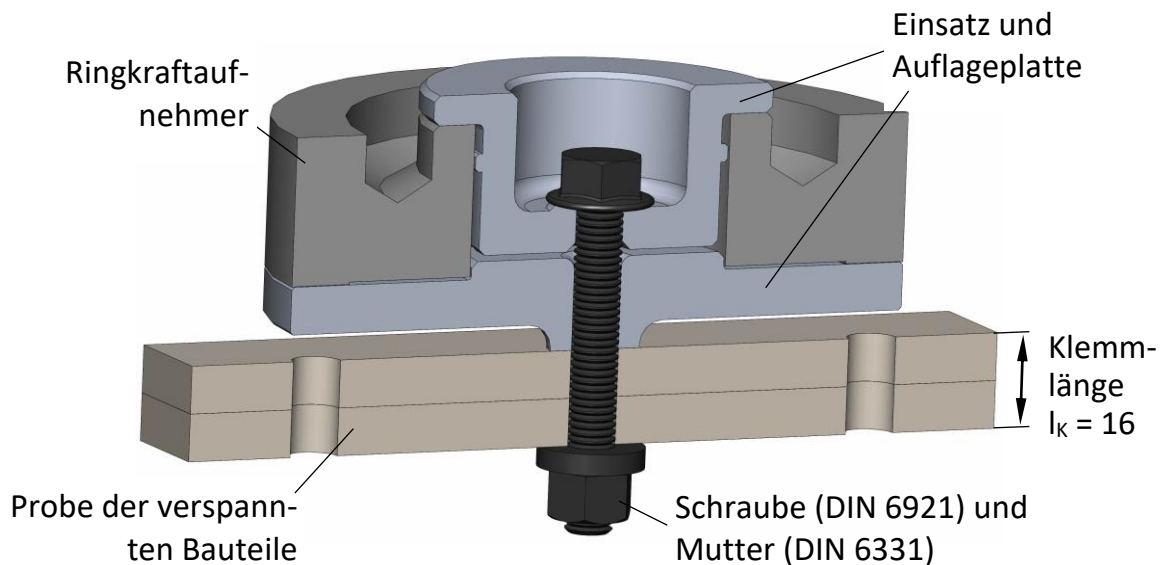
Versuchsaufbau mit Ringkraftaufnehmer, Einsatz, Auflageplatte, Schraube, Mutter und verspannter Bauteilprobe
